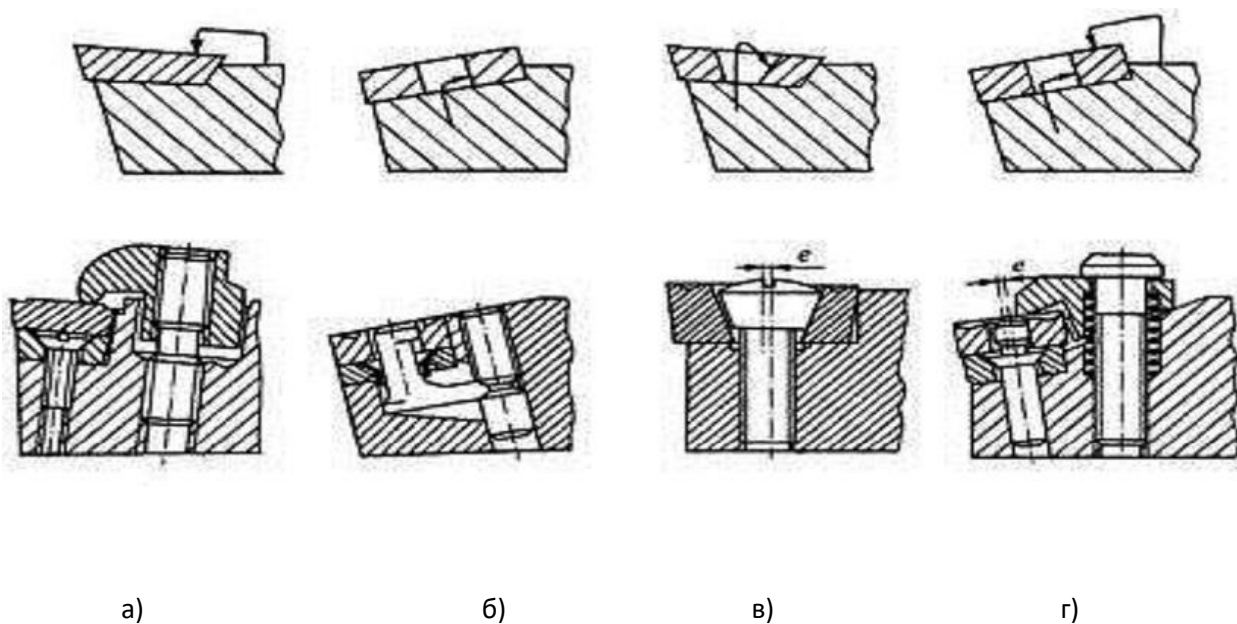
Схемы механического крепления твердосплавных СМП: а – прихватом сверху; б – рычагом через отверстие; в – винтом с конической головкой; г – штифтом через отверстие и прихватом сверху
